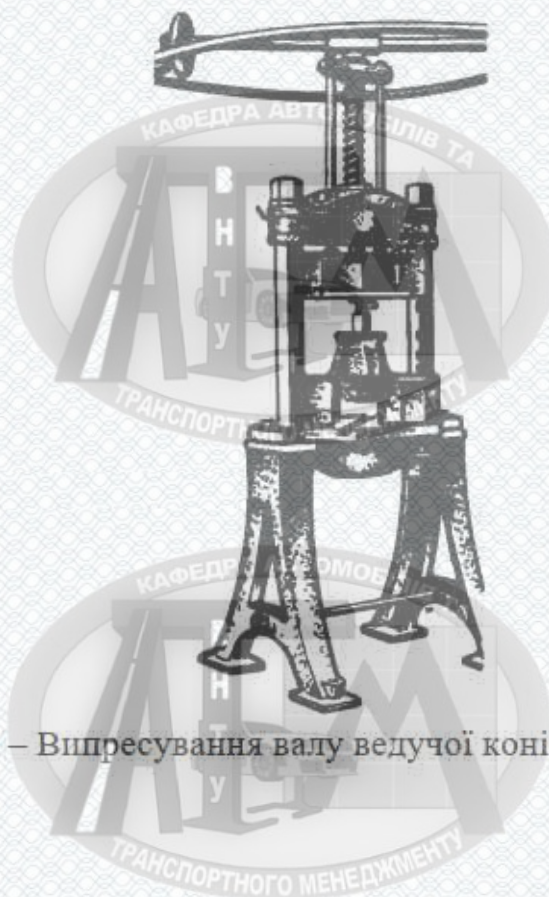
Випресування вала ведучої конічної шестерні [10]
